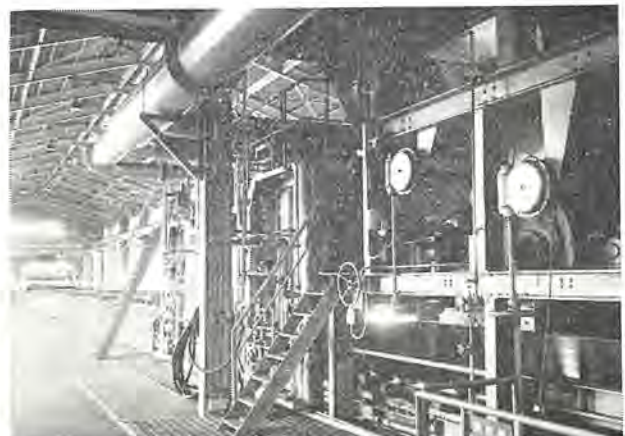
焼結機 Fig. 2.2 Sinter machine.
